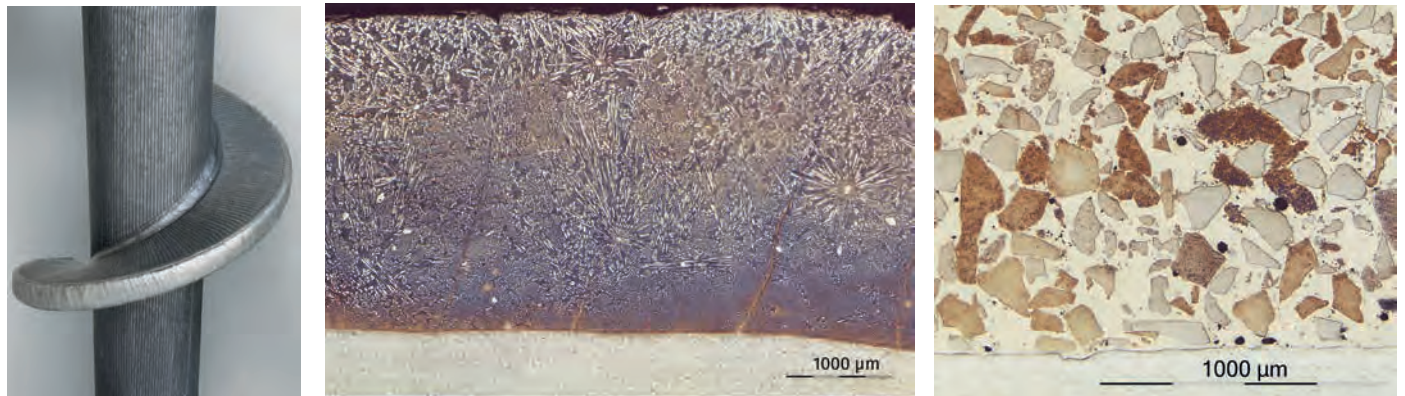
CMT-Auftragschweißung einer Pressschnecke für die Keramikindustrie:
